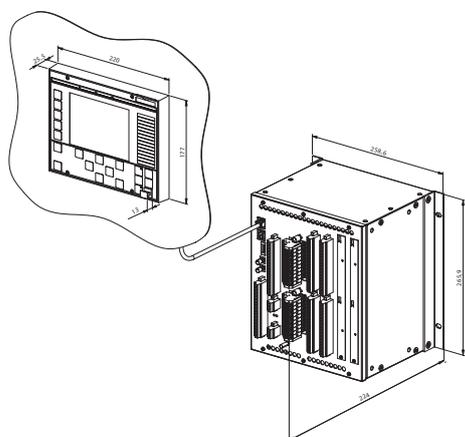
Montage mural d'un boîtier 6U demi 19" avec deux supports de fixation et IHM locale retirée
